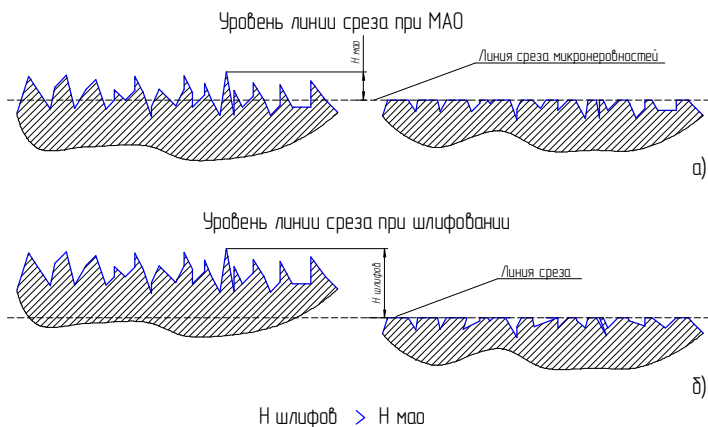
Схема съема металла: а – при MAO, б – при шлифовании
